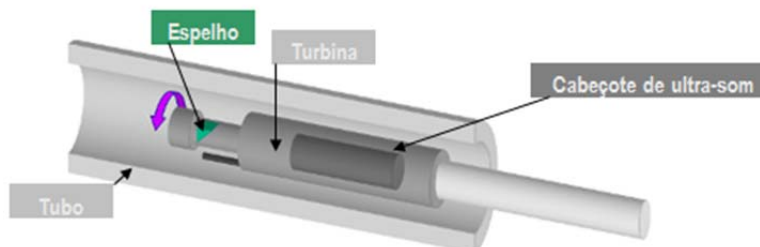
Conjunto utilizado para o ensaio de iris (1)
